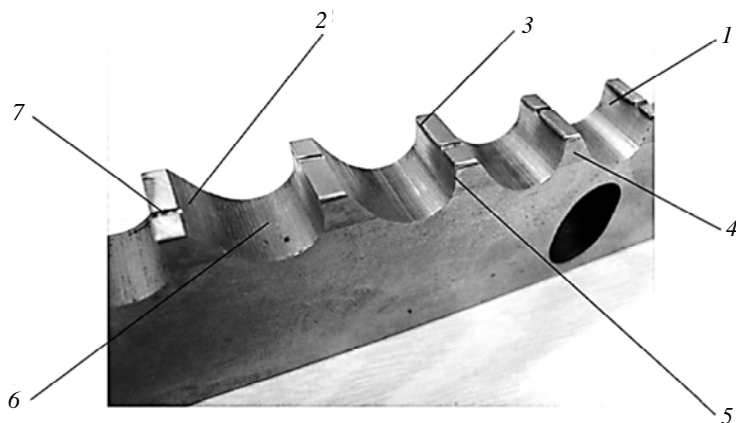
Основные элементы режущей части шпоночной протяжки
